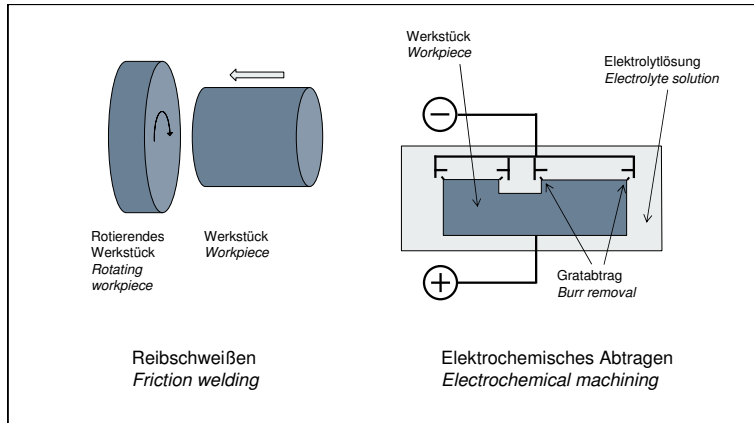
Reibschweißen und ECM-Bearbeitung
